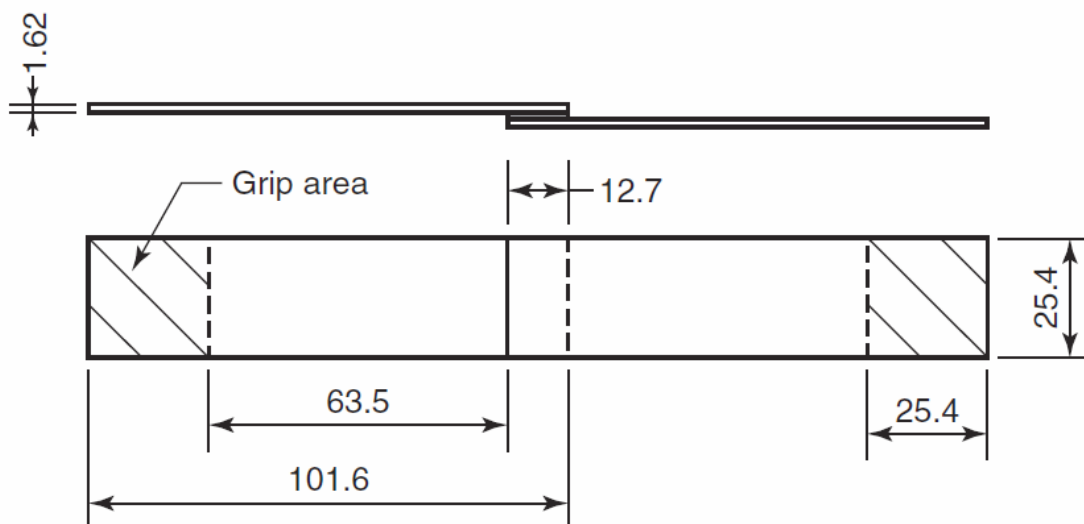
Geometria de uma junta de sobreposição simples (dimensões em mm) [22]
